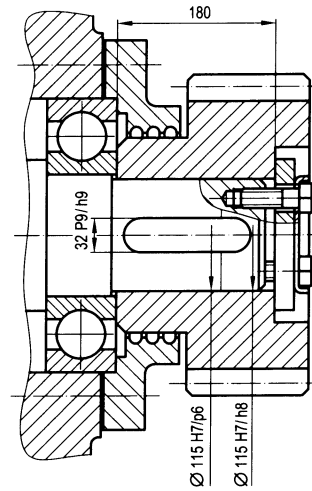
Установка шестерни на цилиндрическом конце вала
